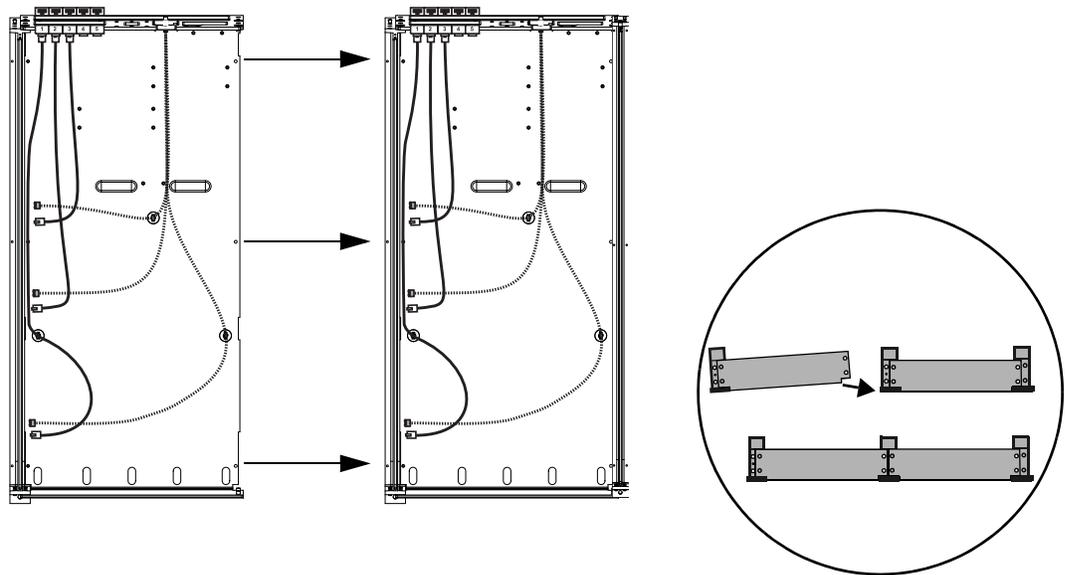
Anbringen der ersten zwei Chassis (Draufsicht, links, und Frontalansicht, rechts)
